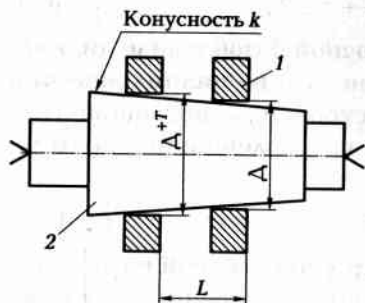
Схема установки детали цилиндрическим отверстием на оправку с малой конусностью
